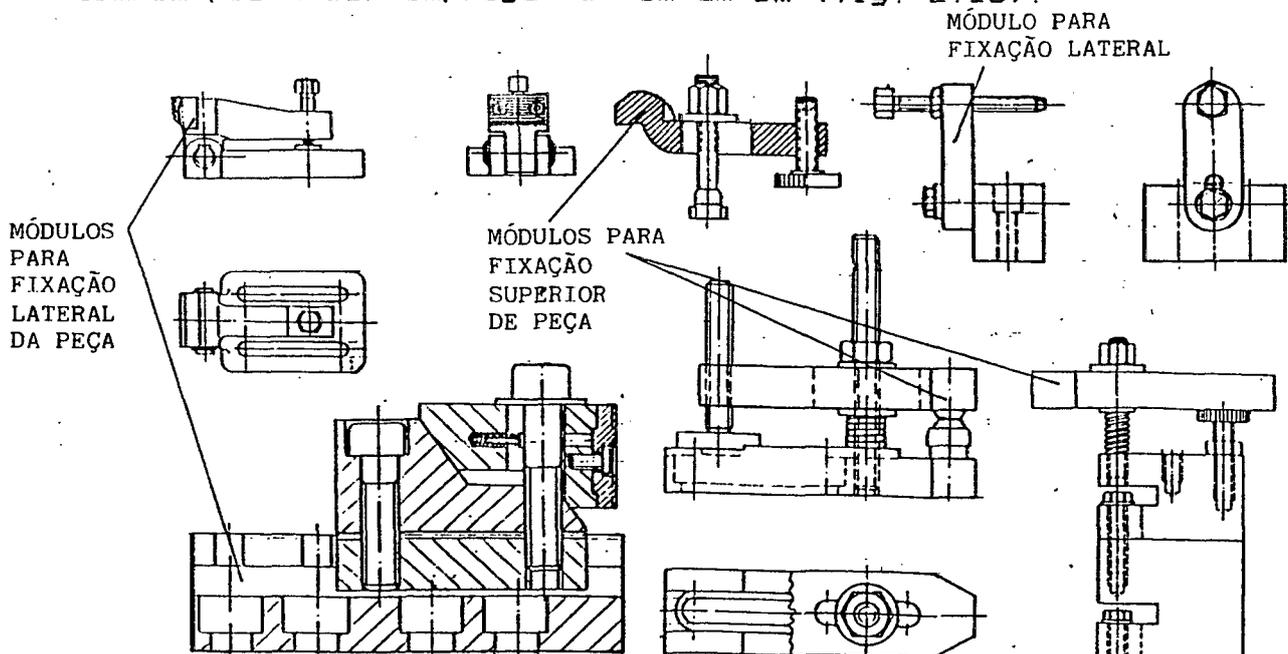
Dispositivos de fixação típicos de conjuntos modulares para processos de fabricação [17,21 e 22].
